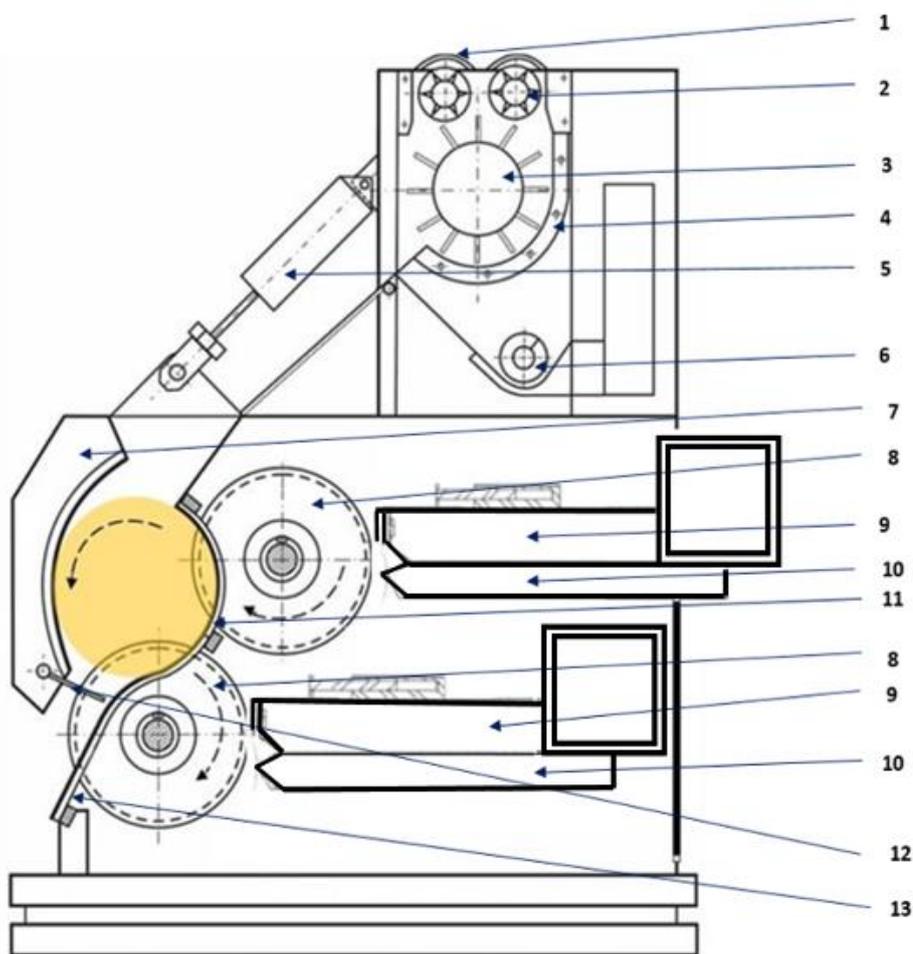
Схема расположения новой конструкции съёмного механизма в однокамерном двухцилиндрном джине:
